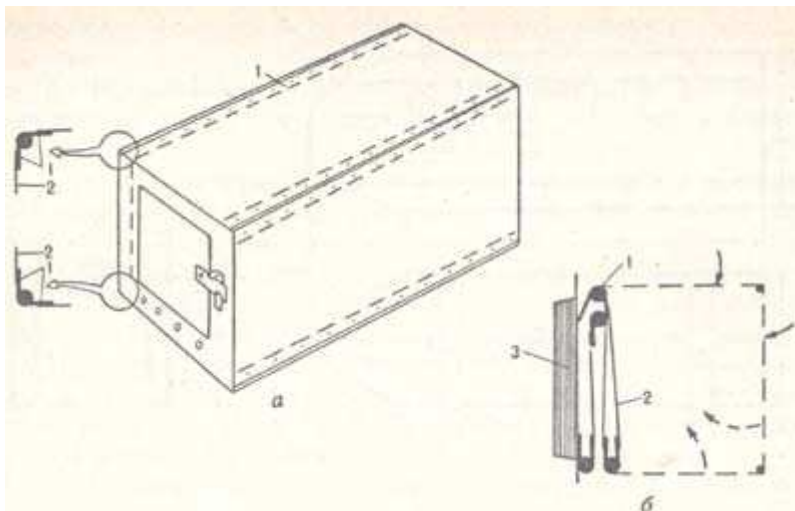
Складная печка на шарнирах: а—общий вид печки (слева—взаимное положение шарниров и стенок); б—печка в сложенном виде. 1—шарниры; 2—стенки печки; 3—торцы.
